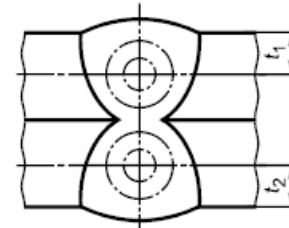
Пример расположения образца для испытаний вдоль шва
